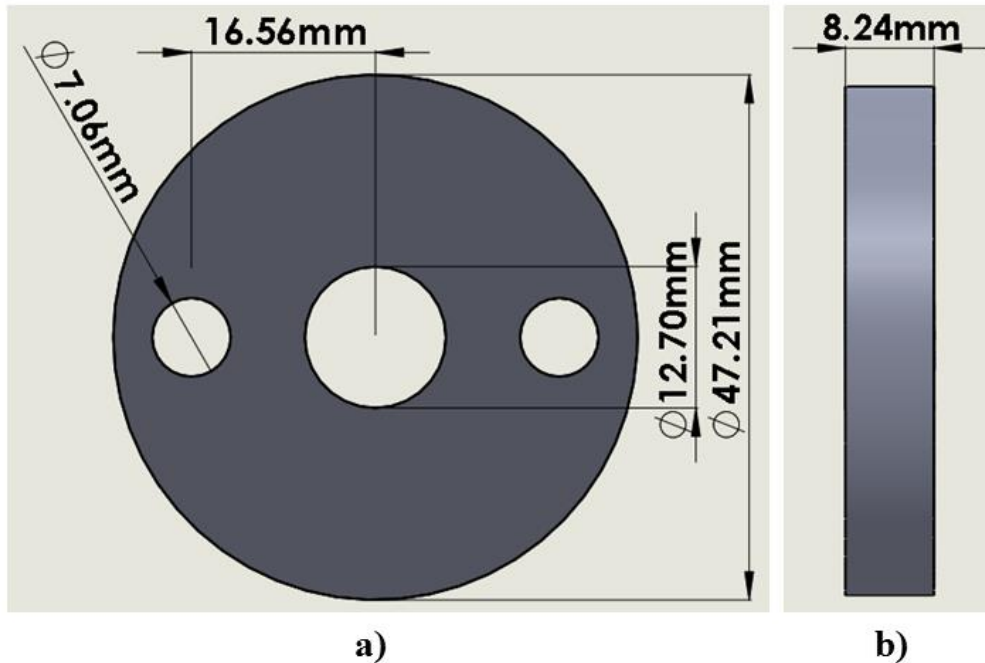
a) Vista frontal de la tapa del rodamiento, b) vista lateral de la tapa del rodamiento.
